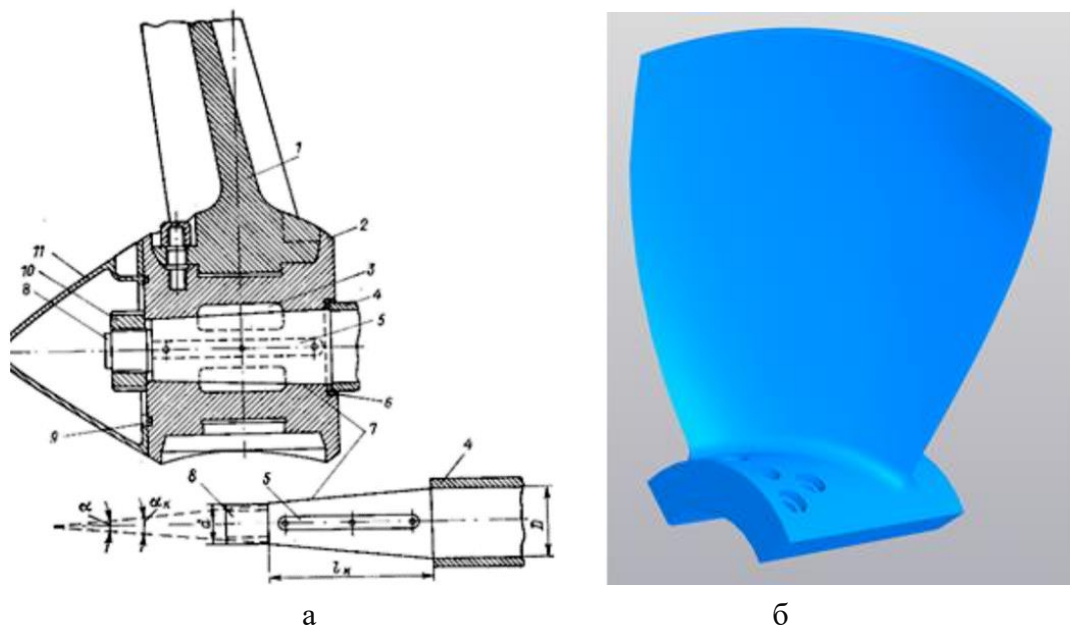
Схема конструкции сборного гребного винта (а) и модель его лопасти (б):
